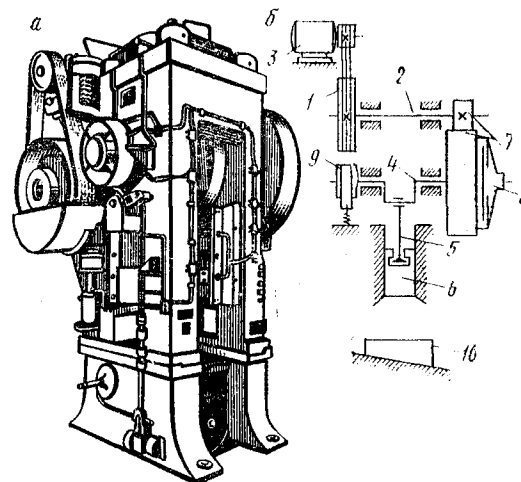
Общий вид кривошипного ковочно-штамповочного прессы (а), его пневматическая схема (б)
